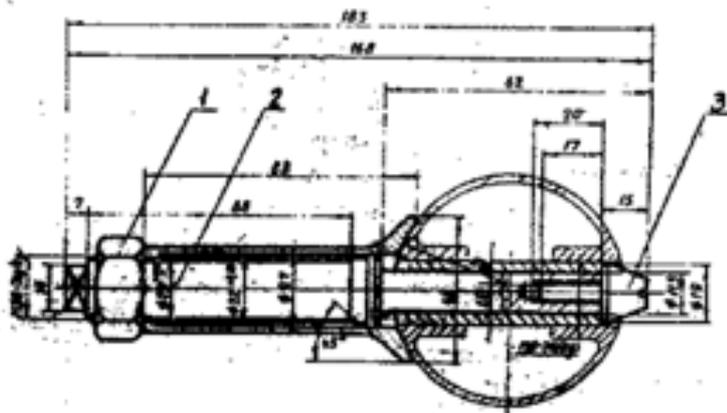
Приспособление для выпрессовки поршневого пальца М9832-077
